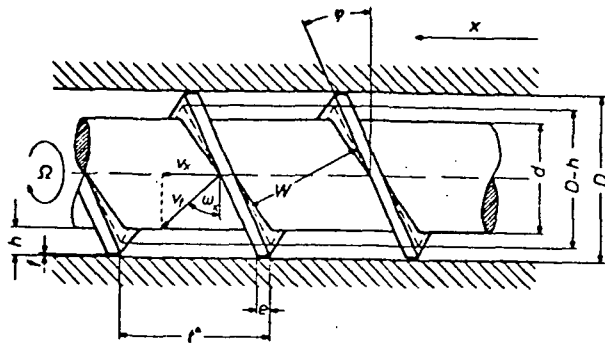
Schneckengeometrie und Definition des Förderwinkels
